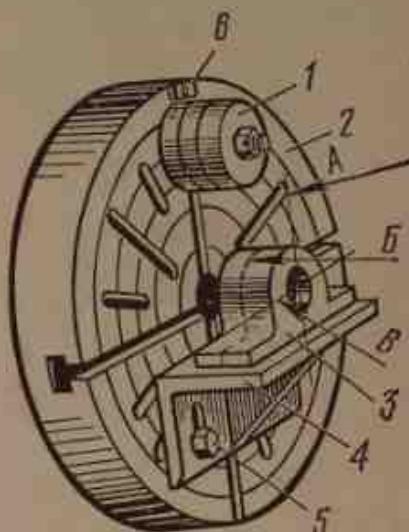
Установка заготовки корпуса подшипника по угольнику:
